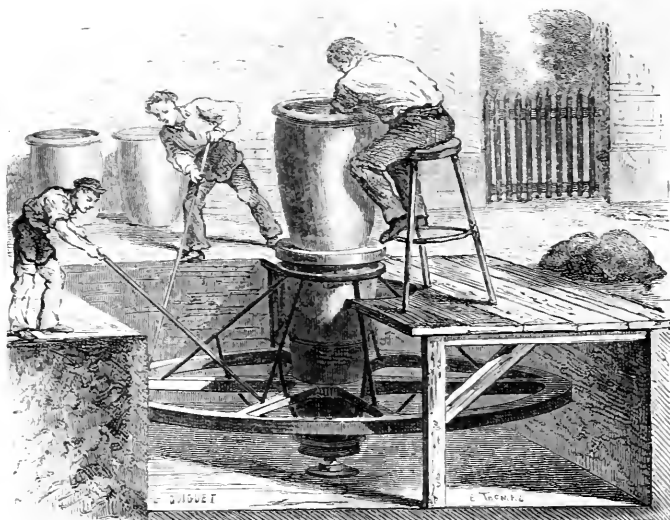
Tournette du potier, ou roue à modeler les pièces de grande dimension.
